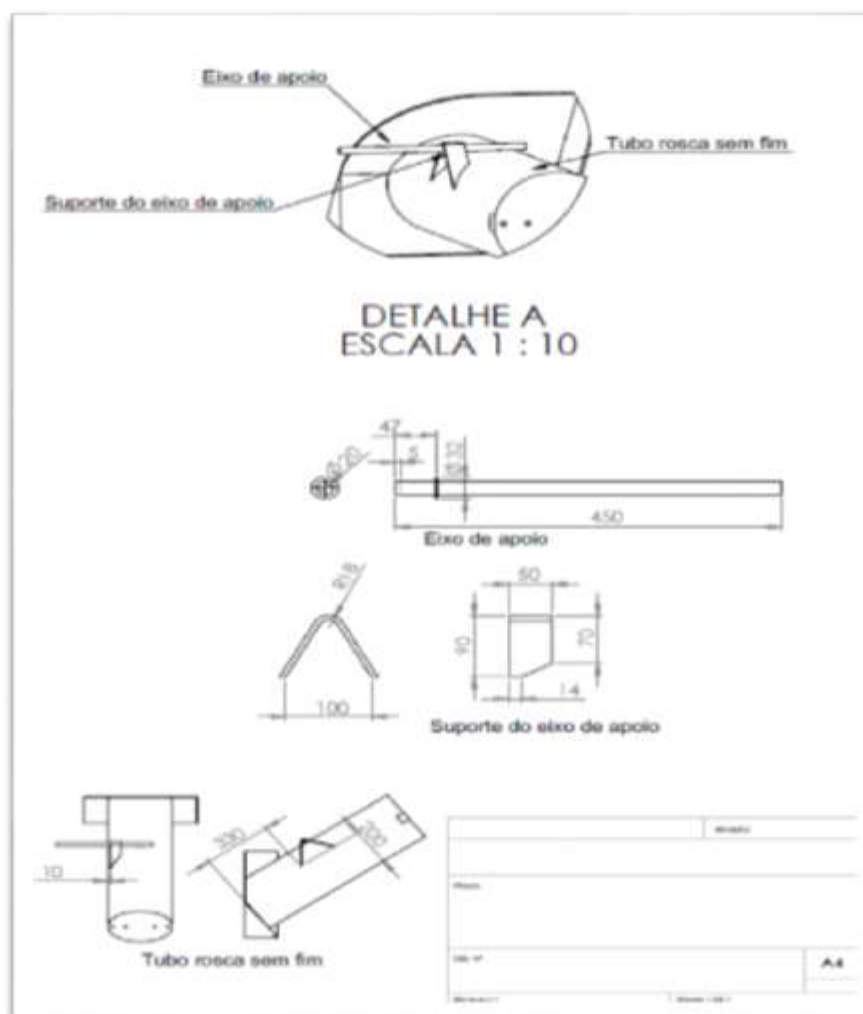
Comando do Suporte Abraçadeira do Sem-fim de Enchimento.
